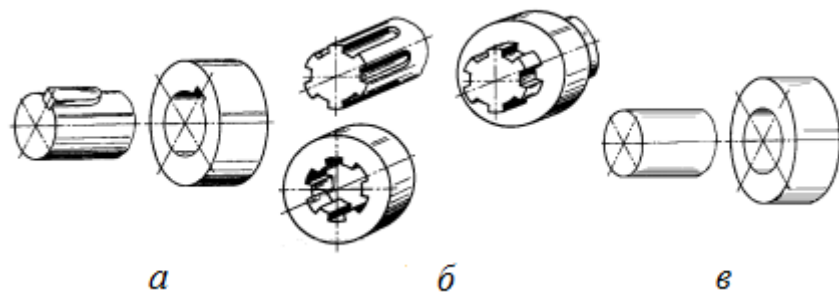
З'єднання вал-втулка: *а* – шпонкове; *б* – шліцьове; *в* – пресове
